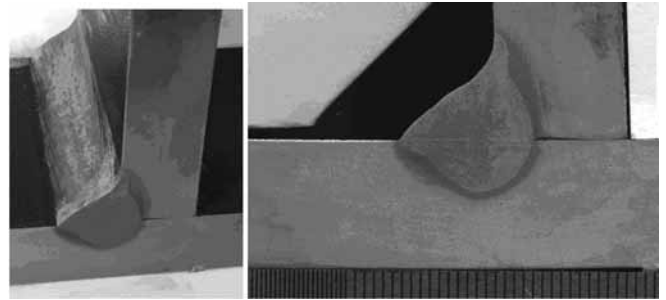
Макрошлиф сварного соединения, полученного при сварке стали 10ХСНД толщиной 14 мм при токе дуги 850 А, напряжении 29 В, скорости сварки 35 м/ч и расположении сварочных проволок согласно рис. 2
